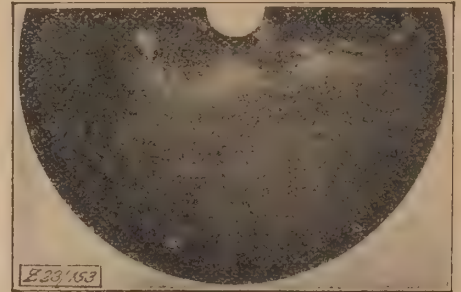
Beiderseits geschlagener Rundkerbstab mit geringem Anriß. Längsschnitt in der Schlagenebene.
